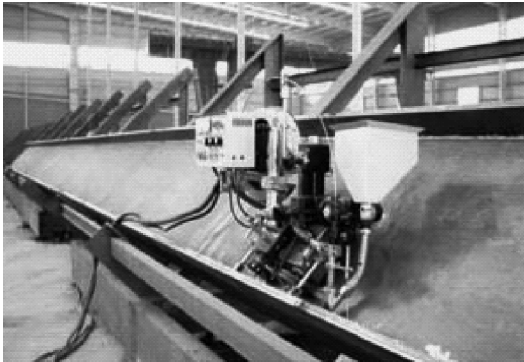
工字梁的角焊缝埋弧焊机
